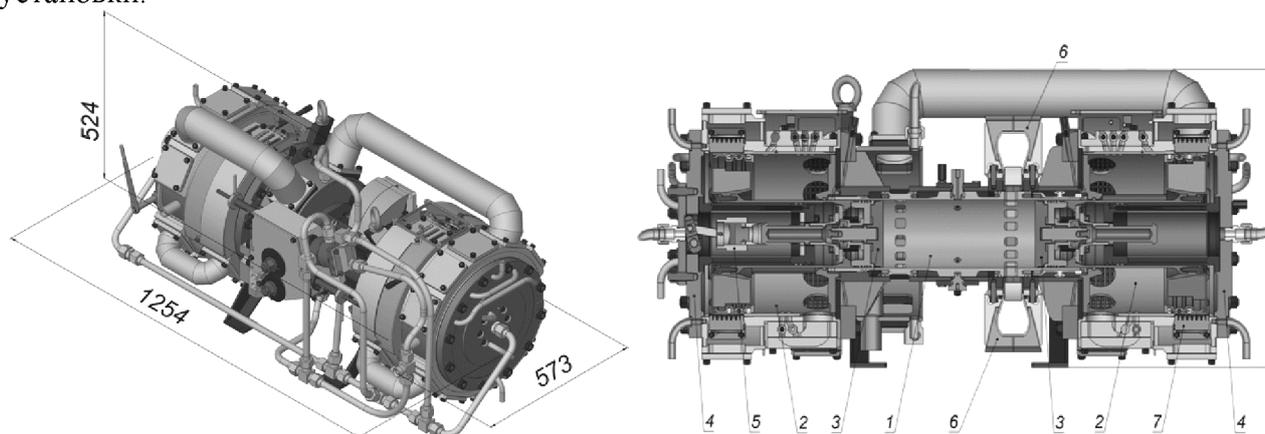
Свободнопоршневой двигатель 1МП120: 1 – остов, 2 – компрессоры, 3 – поршни, 4 – буферные крышки, 5 – механизм пуска, 6 – выхлопные патрубки, 7 – клапаны
